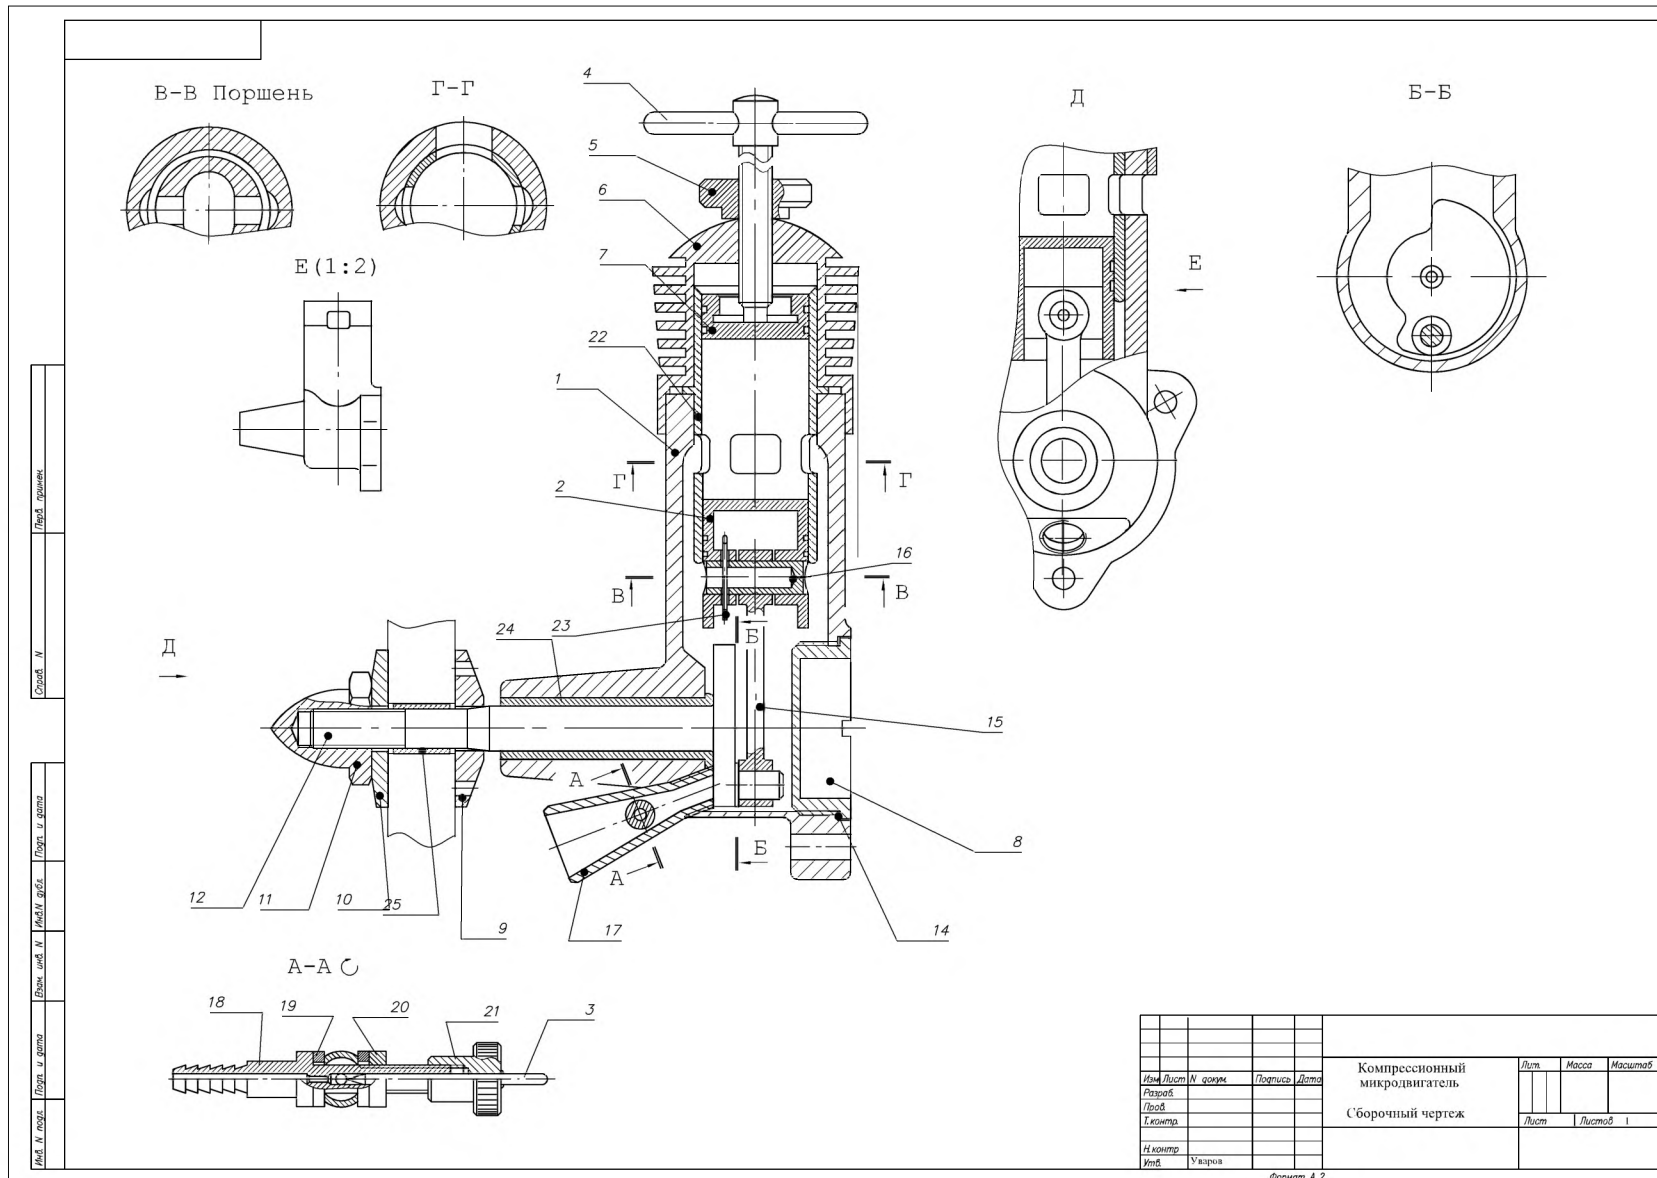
Сборочный чертёж, созданный на «белом листе»
